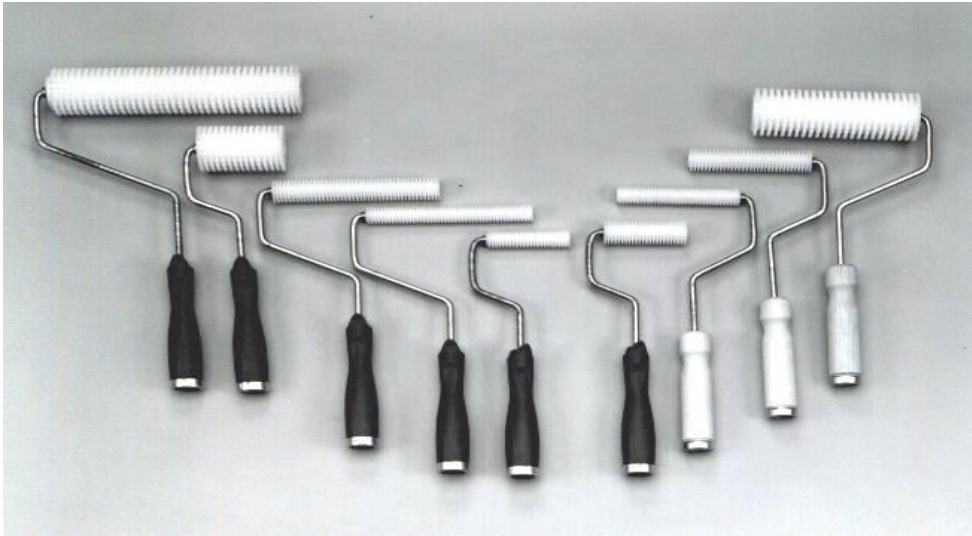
Deluxe & Quick Release Aluminum Bubble Buster
